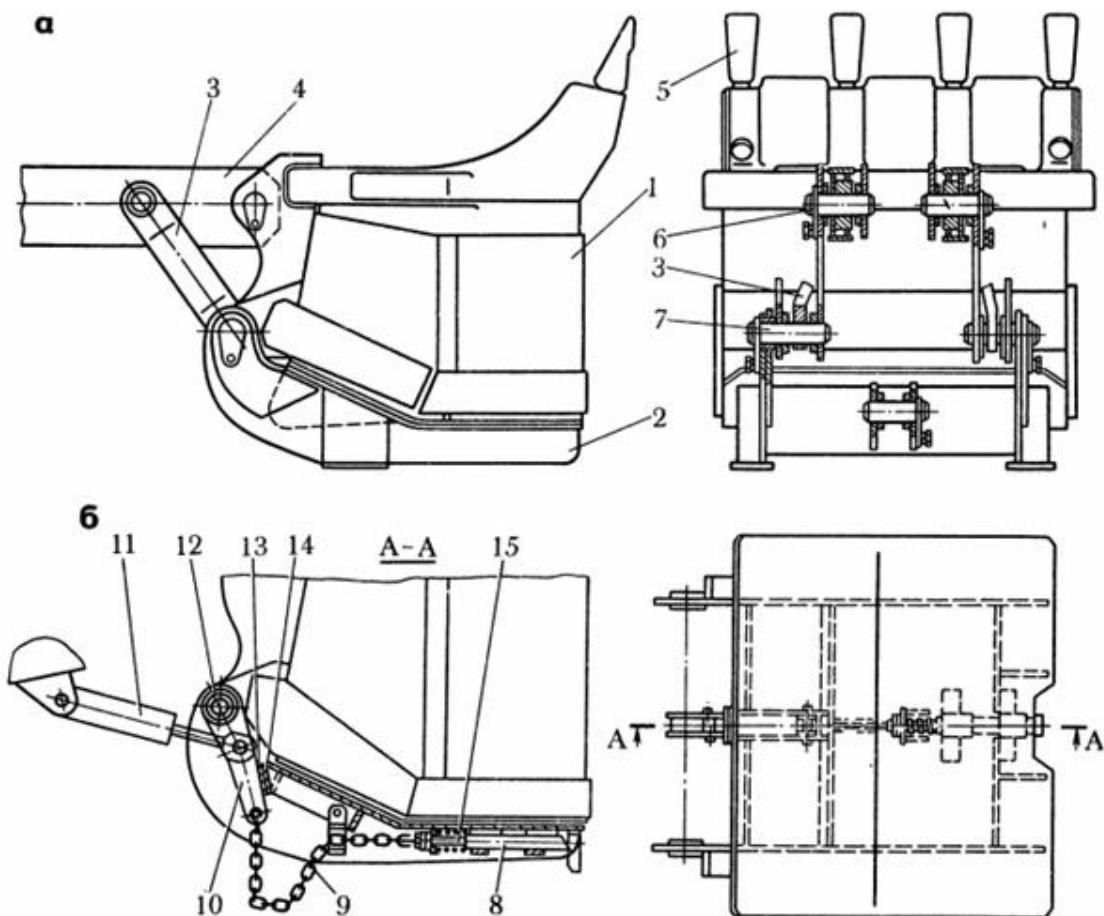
Неповоротный ковш прямой лопаты экскаватора ЭО-4121
